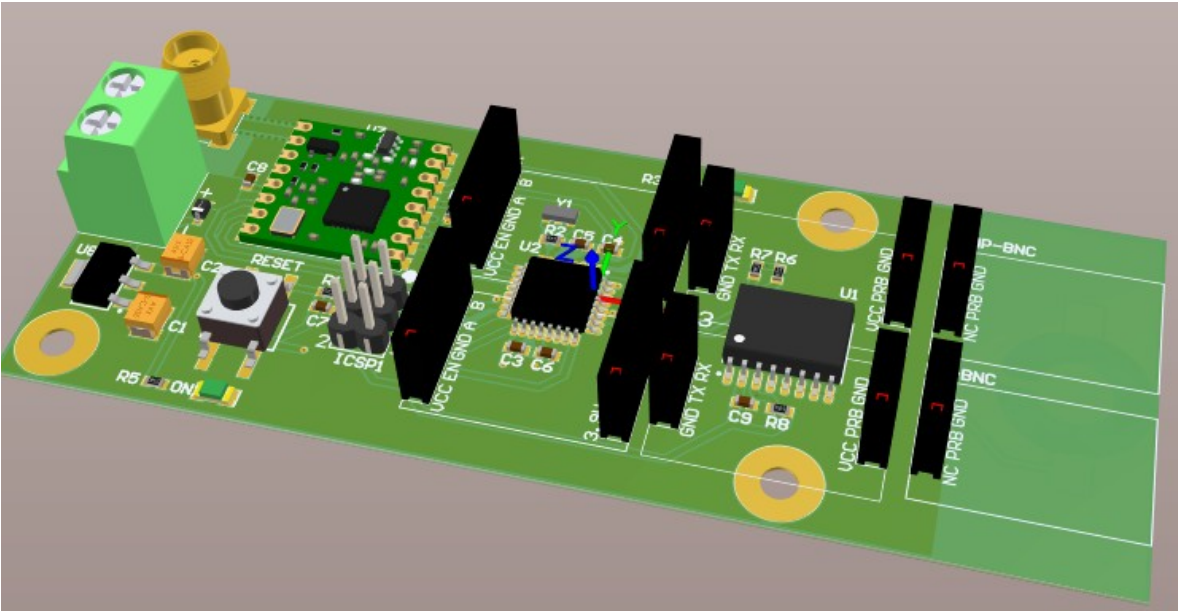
33 Diseño PCB, vista isométrica 3D.
